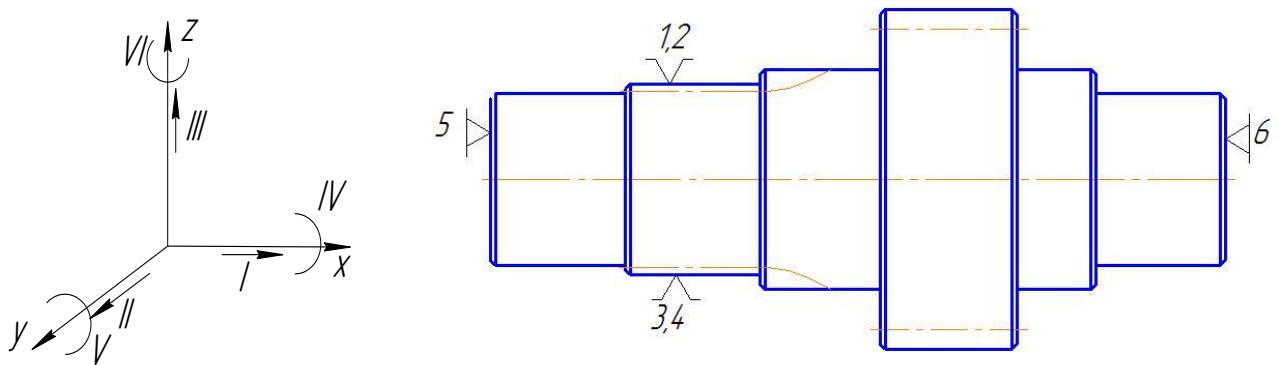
Ескіз обробки заготовки на операції 005
